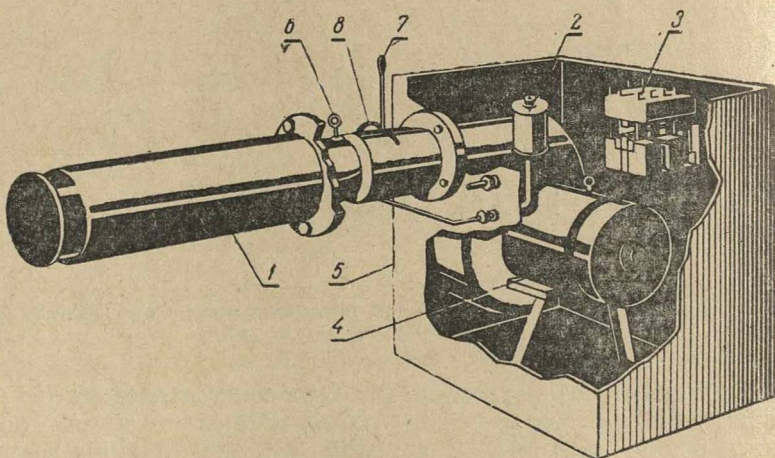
Приспособление ПНГ—ВИЭСХ: 1—горелка; 2—соленоидный клапан; 3—магнитный пускатель; 4—электродвигатель с вентилятором; 5—монтажный ящик; 6—пробка запального отверстия; 7—рукоятка для регулирования подачи воздуха; 8—топливный вентиль.
